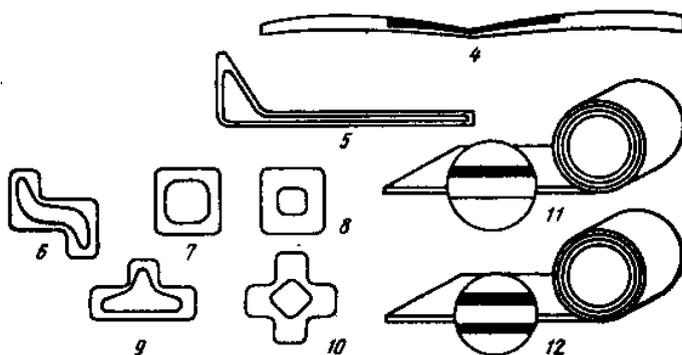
Поперечные сечения профилей сварных конструкций:
